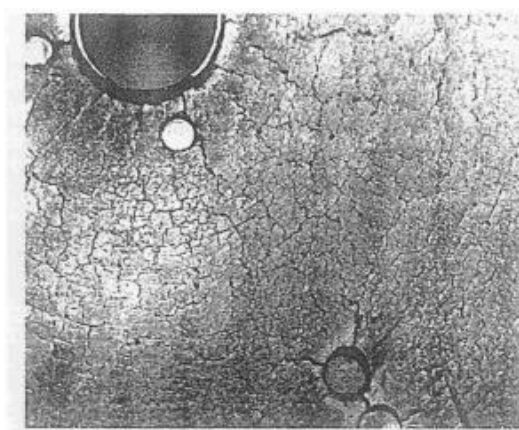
Разгарные трещины на поверхности отливки
